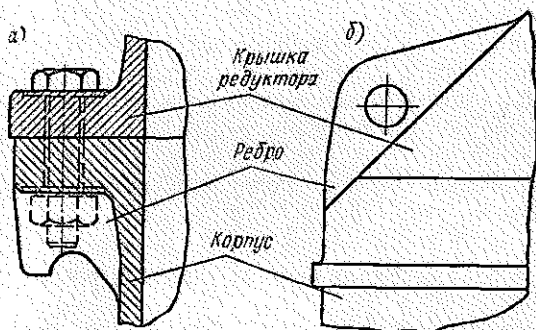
Устройства для подъема и транспортировки корпусных деталей: а — грузовой крюк на ребре корпуса; б — проушина в ребре крышки редуктора
